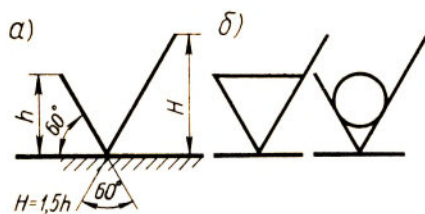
Обозначение шероховатости поверхностей на чертеже
